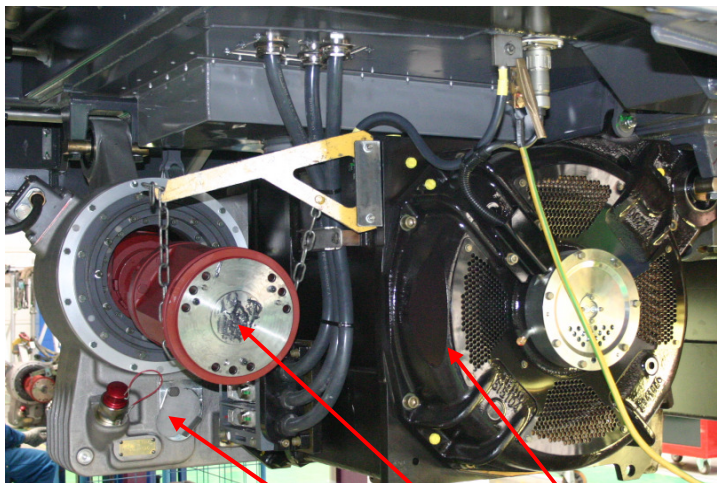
Getriebe - Tripode - Fahrmotor
